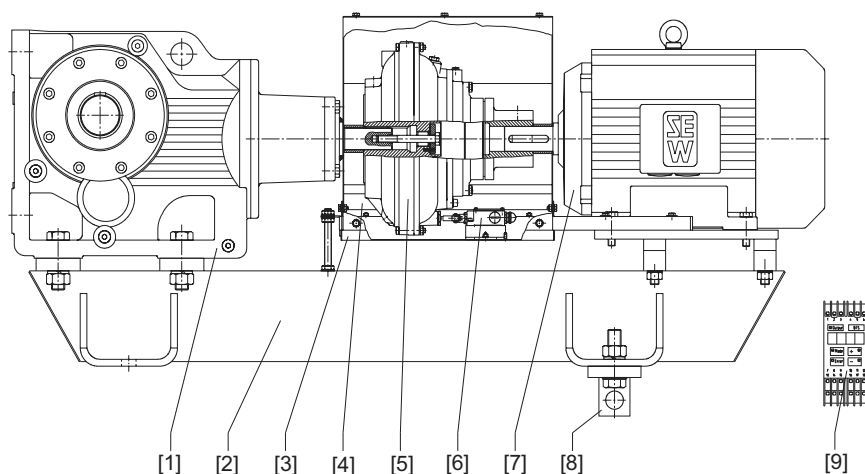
Redutor de engrenagens cónicas em base oscilante MK
